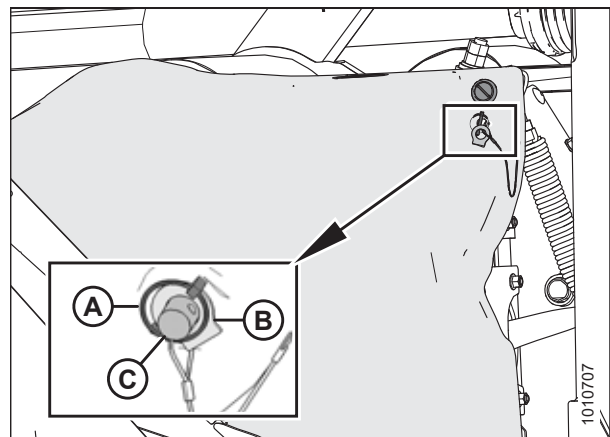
Outil pour déverrouiller la protection de la transmission
